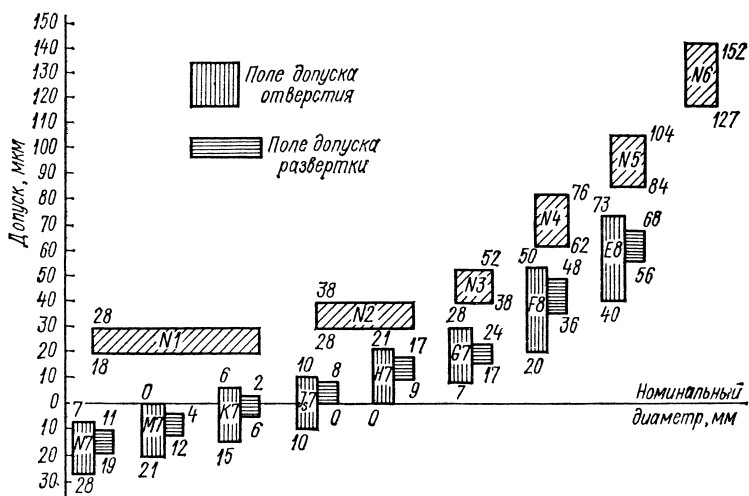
Схема расположения допусков на отверстия и развертки для их обработки
